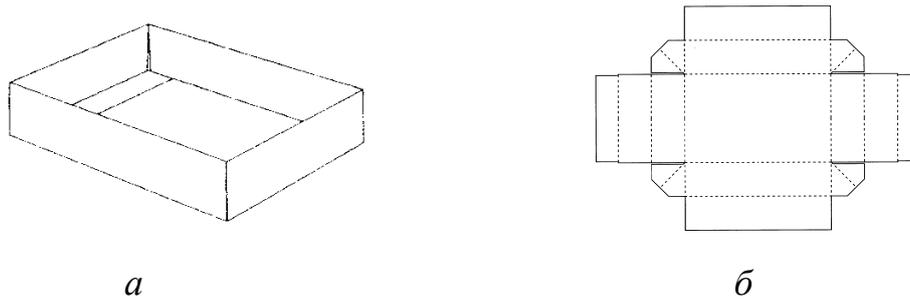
Внешний вид (а) и развертка (б) лотка с самозакрывающимися двойными стенками
